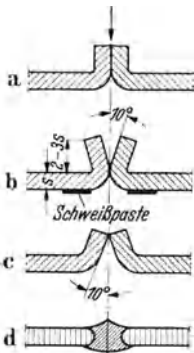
Vorbereitung der Blechkanten zum Festschweißen.
